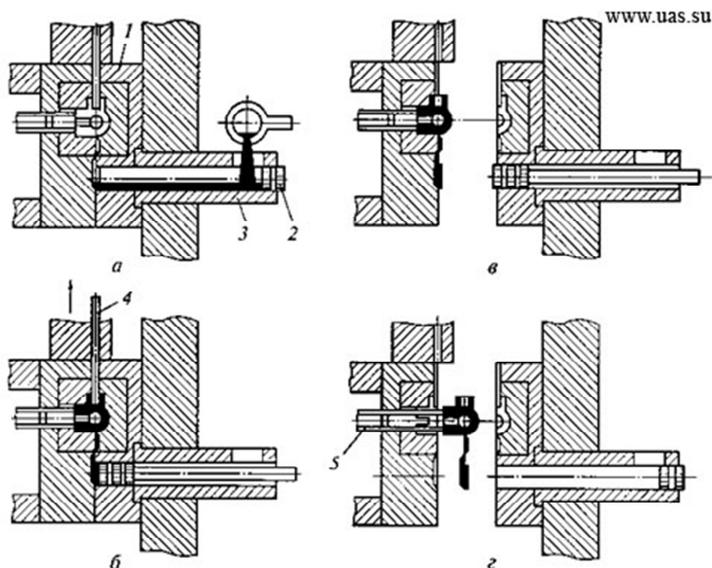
Схема технологического процесса литья под давлени-ем на машине с холодной камерой прессования: а – подача расплава в камеру прессования; б – запрессовка; в – раскрытие пресс-формы; г – выталкивание отливки; 1 – пресс-форма; 2 – пресс-поршень; 3 – камера прессования; 4 – стержень; 5 – толкатель
